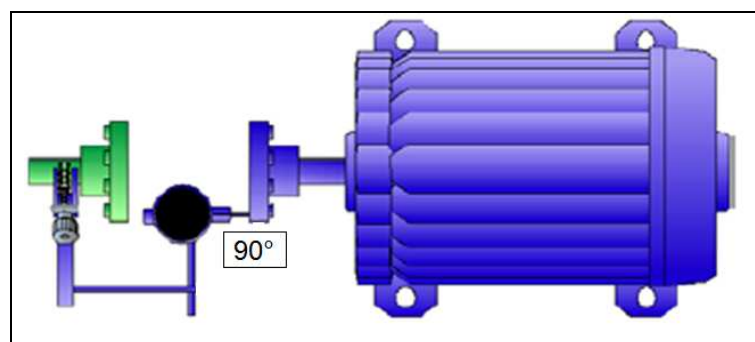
Posición 90° de medición FACE. Vista superior de motor.
